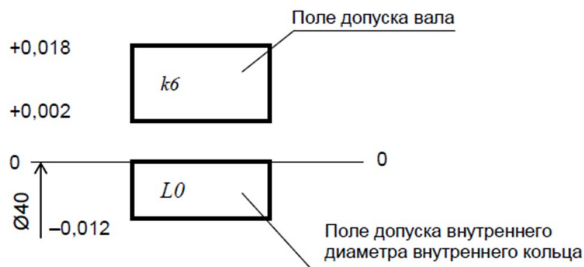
Схема полей допусков сопряжения вала и внутреннего кольца подшипника качения нормального класса точности
